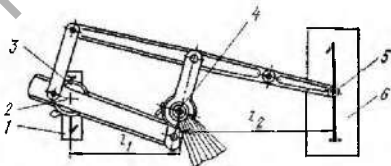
Схема пантографа копировально-фрезерного станка
